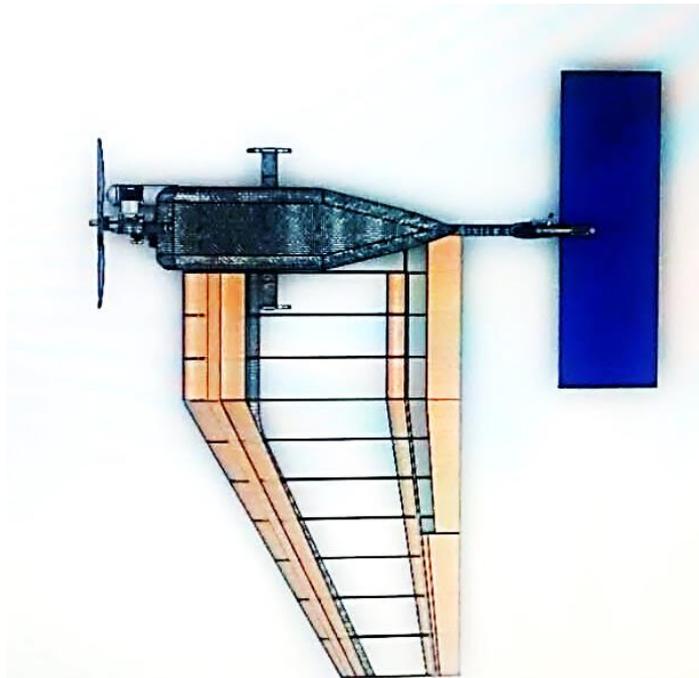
Vista em planta do desenho detalhado da aeronave AGE I
